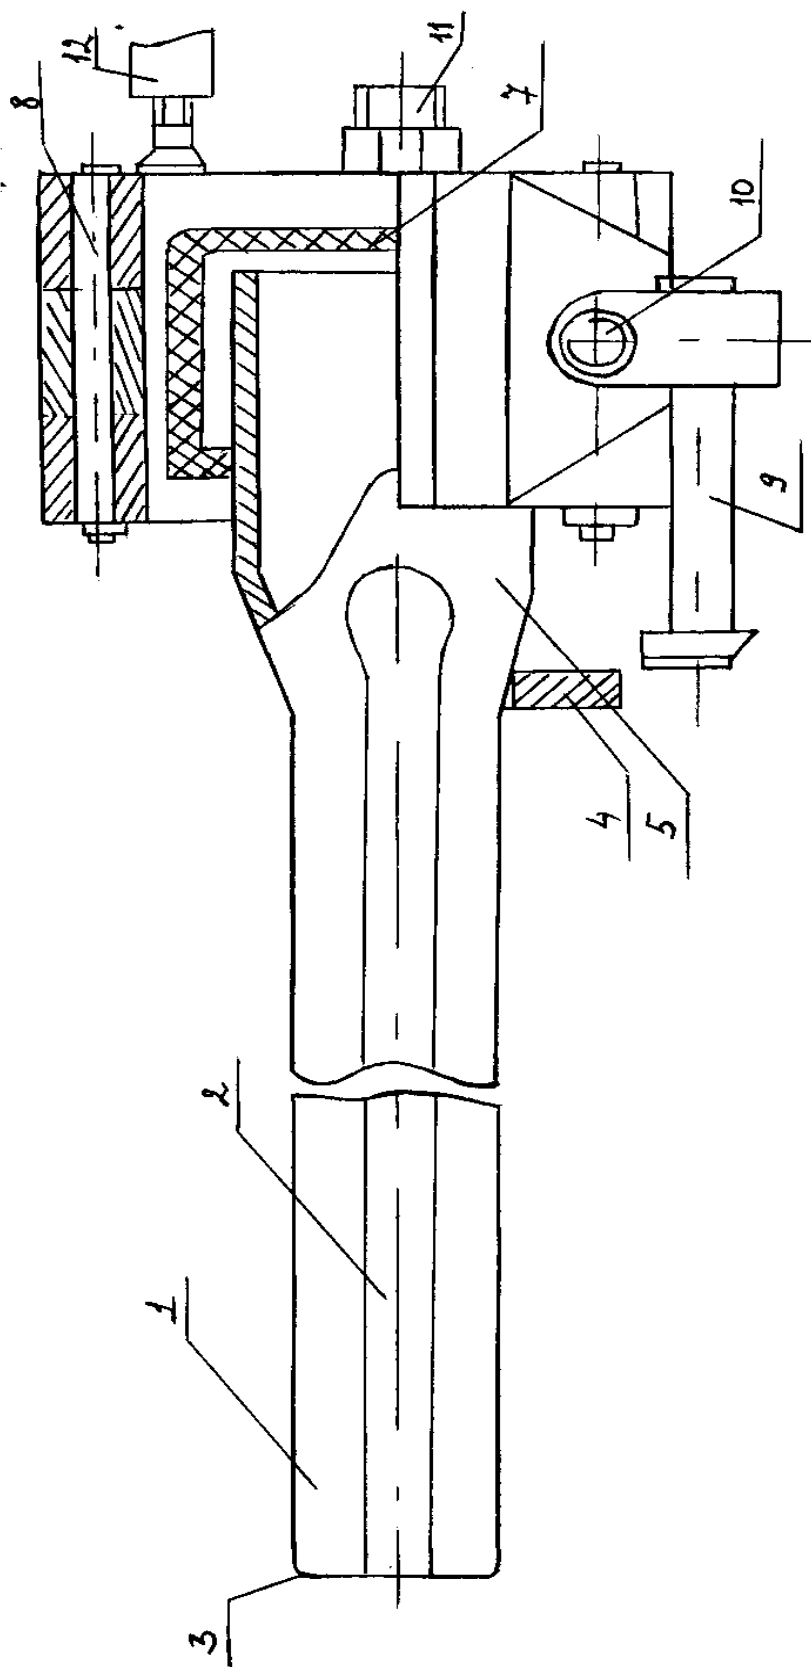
Трубчатый анкер и держатель для его установки
